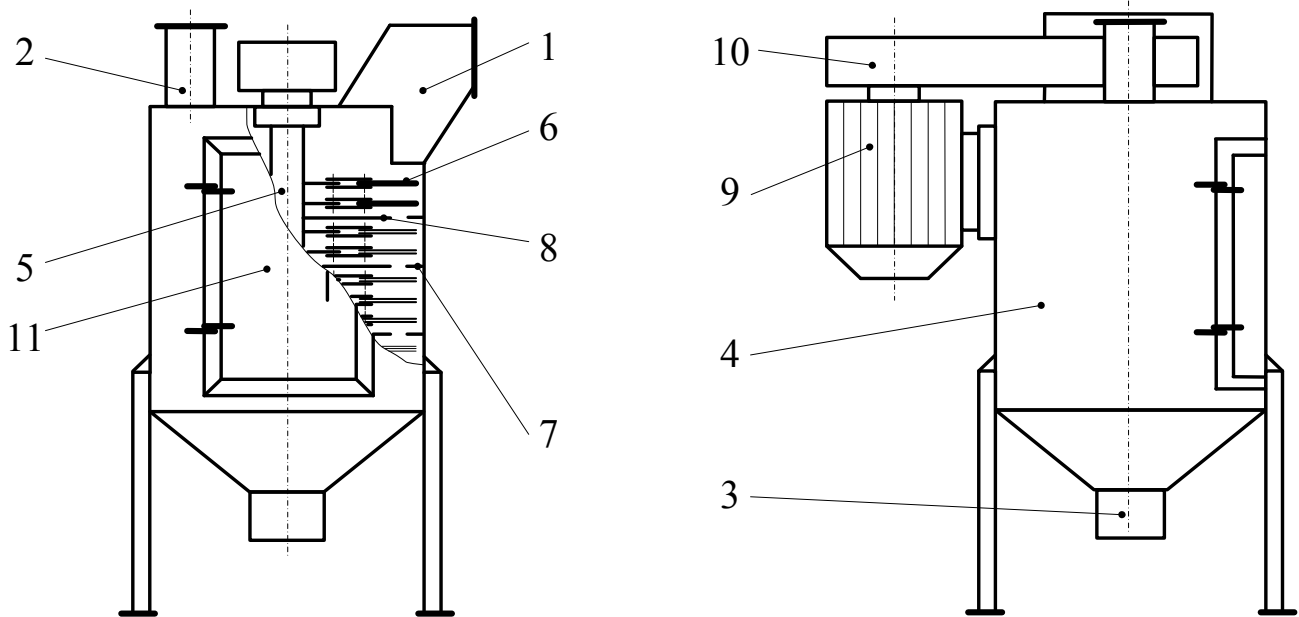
Конструктивная схема измельчителя "ИХ-500"
